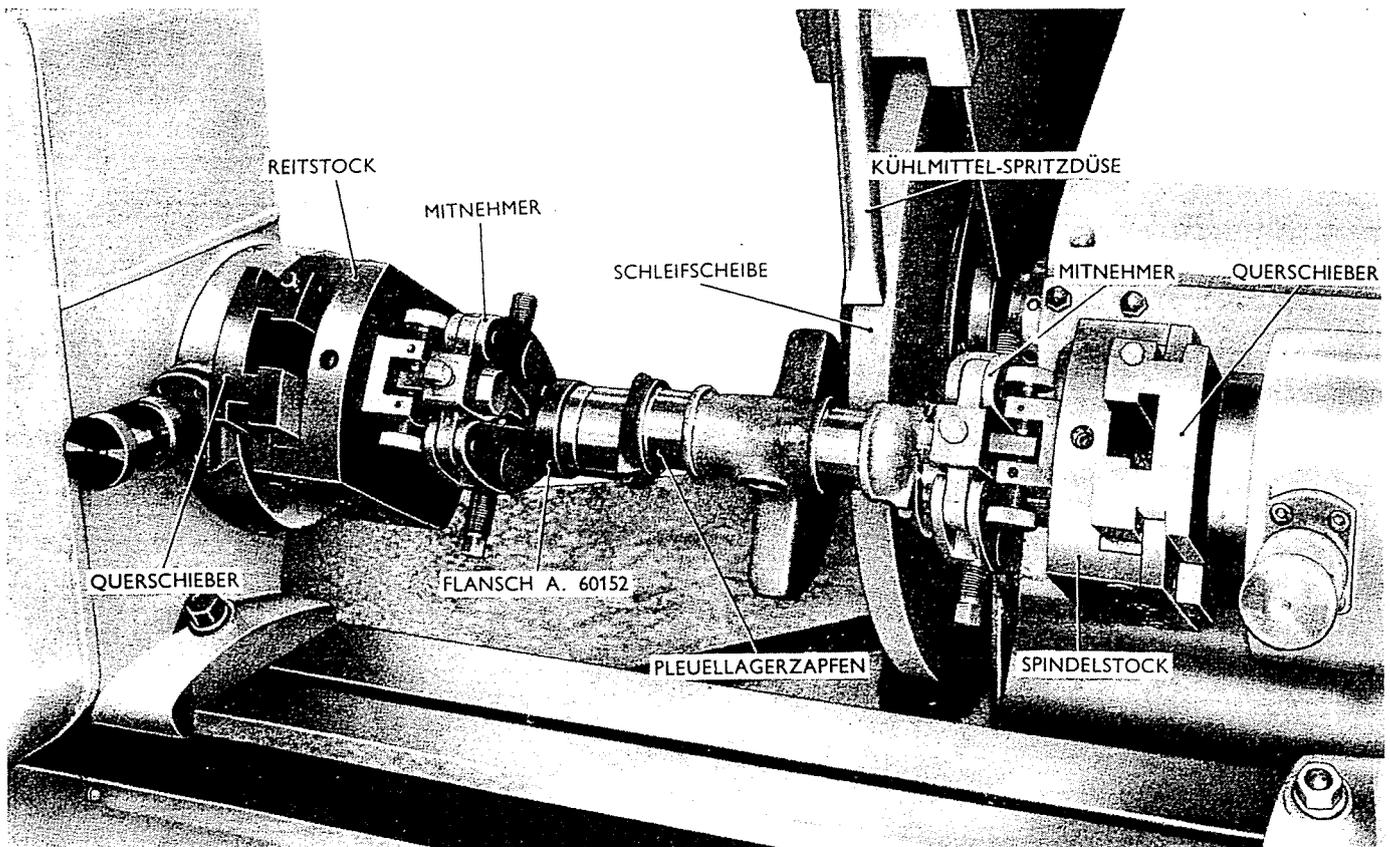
Schleifen der Pleuellagerzapfen auf der Schleifmaschine.
